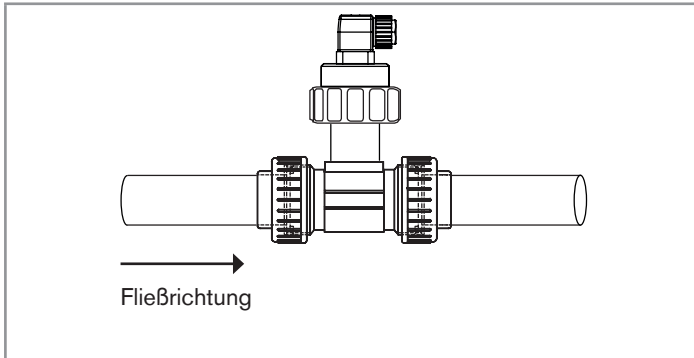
Einbauposition von Fitting mit Gerät auf der Rohrleitung
